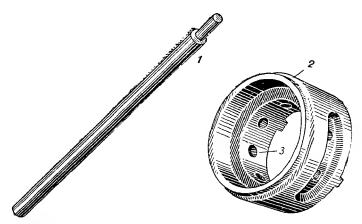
Ключ для завертывания гайки коллектора: 1 — вороток; 2 — нажимная втулка; 3 — корончатая втулка.
